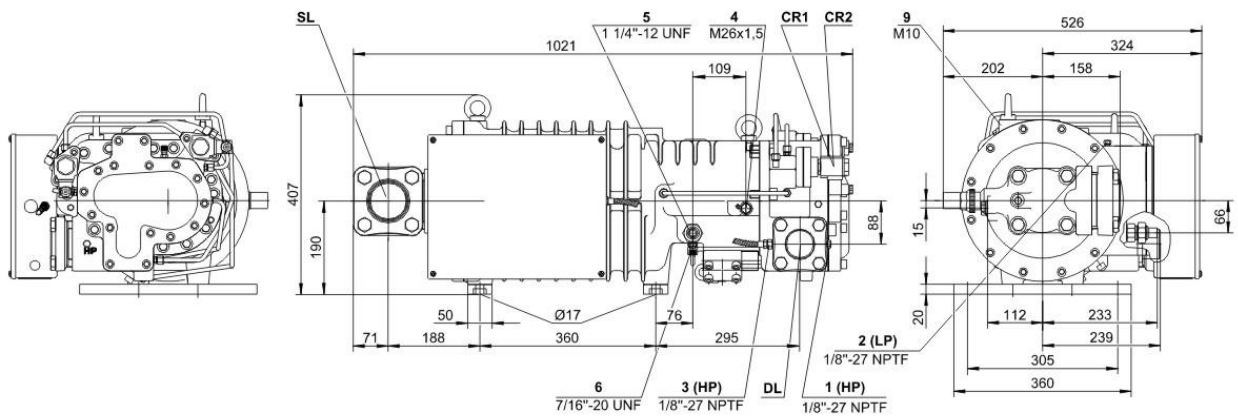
Загальний вигляд компресора Bitzer HSK7451-50
